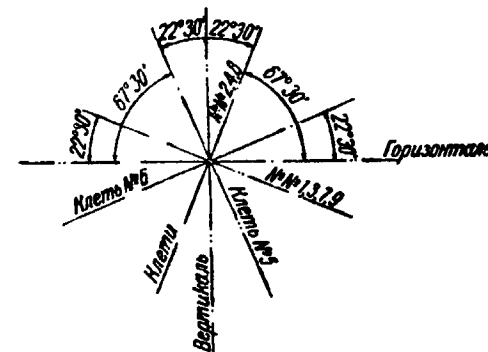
Схема расположения осей валков в непрерывном стане второго типа
